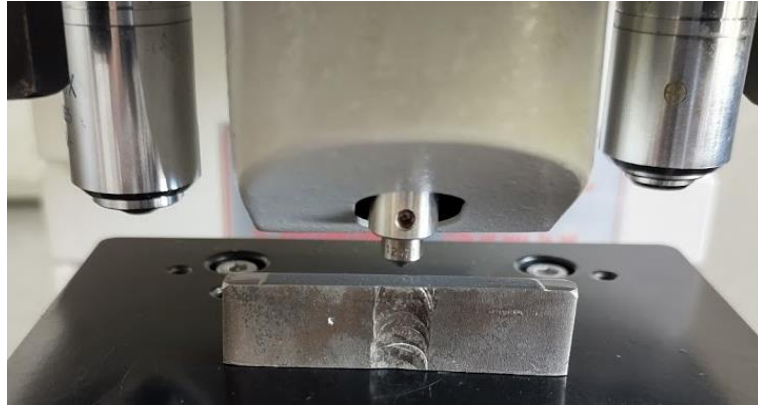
Ensayo de resistencia a la microindentación en soldaduras GTAW. Probeta soldada con material de aporte.
